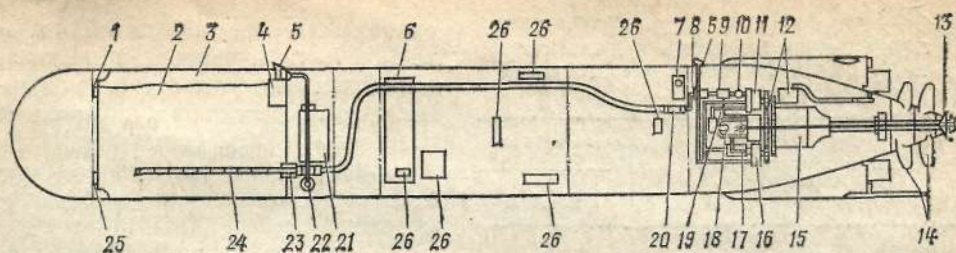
Схема американской двухцелевой торпеды NT 37С: 1 — воздушный клапан; 2 — топливный бак; 3 — компенсирующий объем; 4 — регулятор давления; 5 — отверстие для забора воды; 6 — панель акустической системы самонаведения; 7 — коробка управления двигателем; 8 — отсекающий клапан топлива; 9 — блокировочный клапан топлива; 10 — соленоидный клапан; 11 — топливный насос; 12 — система управления торпедой; 13 — выхлопной клапан; 14 — винты; 15 — двигатель; 16 — водяной насос; 17 — спускной клапан воды; 18 — камера сгорания; 19 — воспламенитель; 20 — разъем; 21 — аккумуляторная батарея; 22 — вспомогательная система создания давления в топливном баке; 23 — быстроразъемный соединитель; 24 — труба для забора топлива; 25 — дренажный клапан; 26 — приборы наведения и управления торпедой
